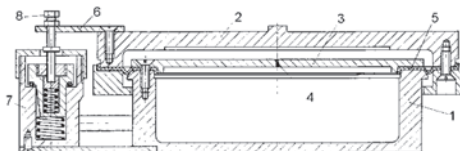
Конструктивная схема пневматической виброизолирующей системы:
